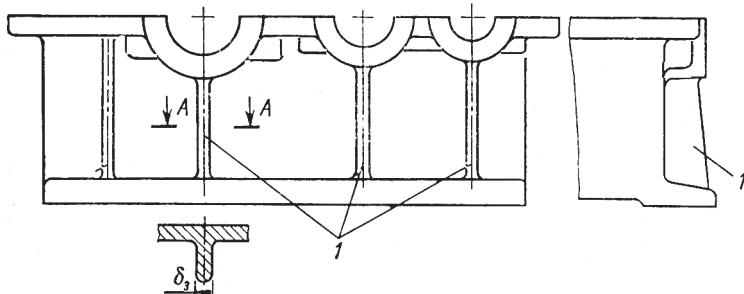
Упрочнение корпуса редуктора ребрами
